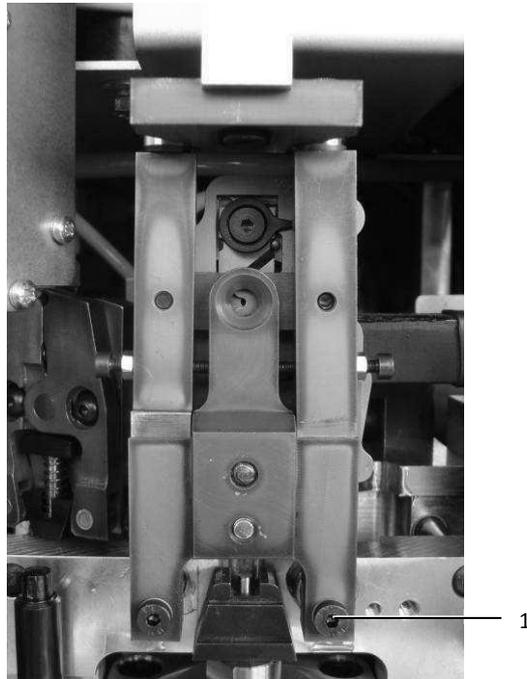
Hülsenhaltezange und Crimpwerkzeug
